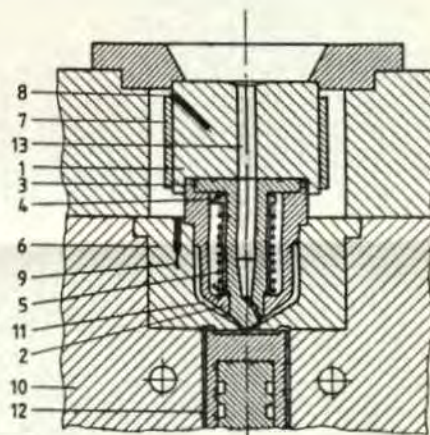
Detalle de un molde experimental con boquilla con canal caliente, sistema Thermoplay
